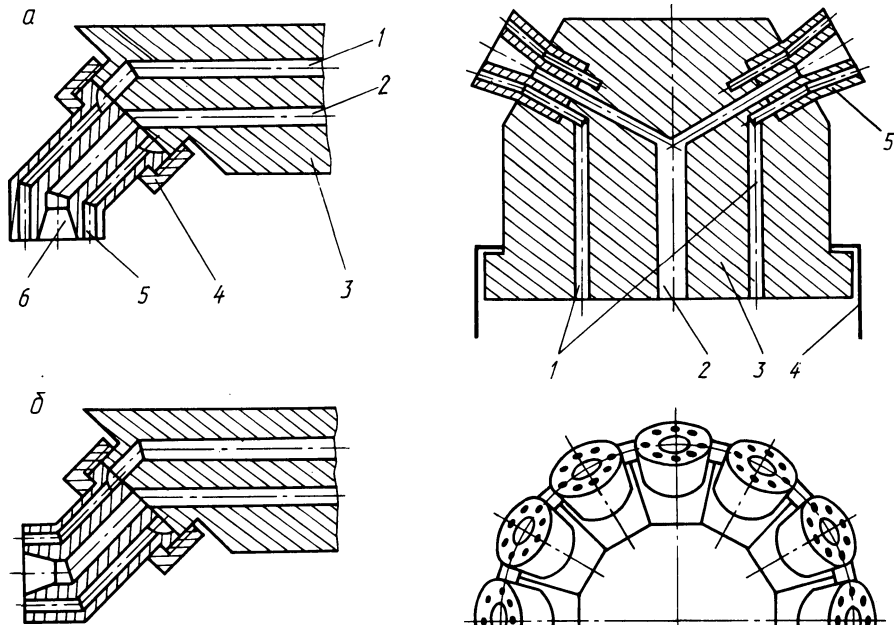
Поворотное сопло: 1 – канал для подачи рабочих газов; 2 – канал для подачи порошка; 3 – угловая головка; 4 – накидная гайка; 5 – сопловые каналы; 6 – центральный канал.
